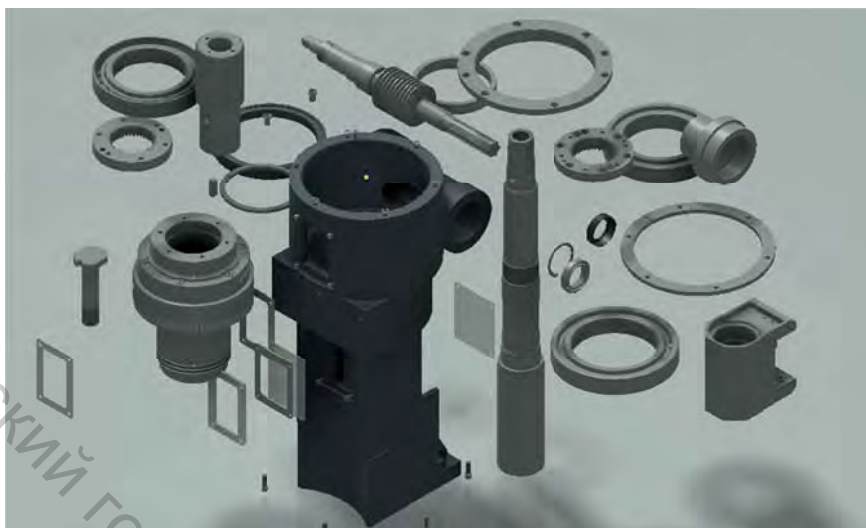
Суппорт полуавтомата зубофрезерного вертикального ВС-122
